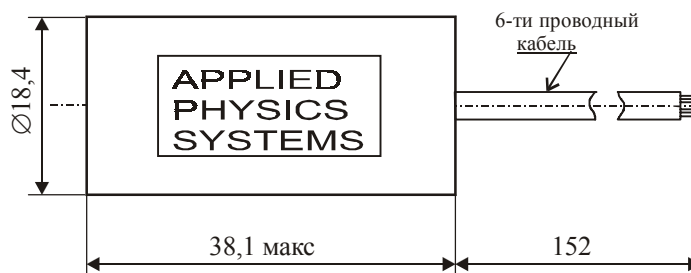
Внешний вид и габаритные размеры датчика типа APS-533
